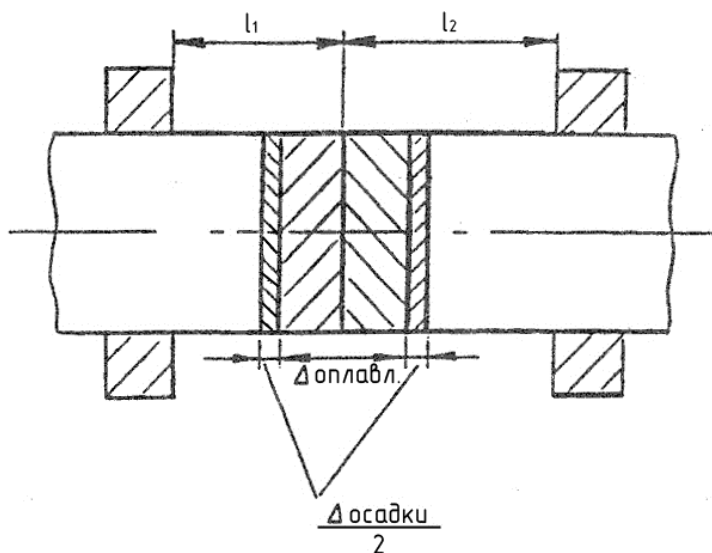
Схема стыковой сварки оплавлением
